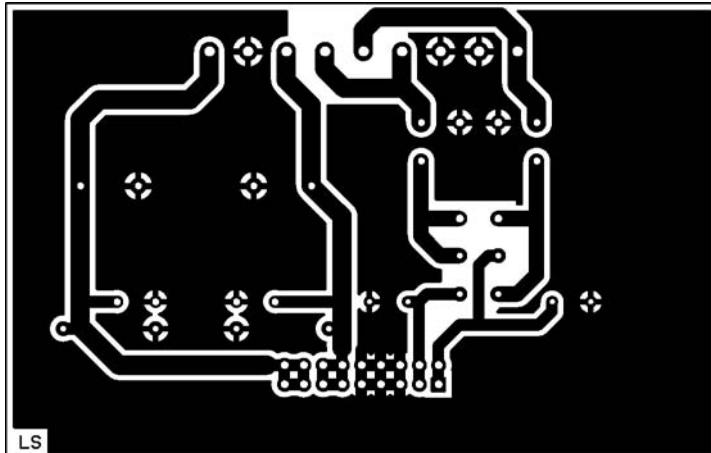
1: Dessin à l'échelle 1 du circuit imprimé double face du Module de filtrage de l'alimentation de laboratoire professionnelle, côté soudures.
